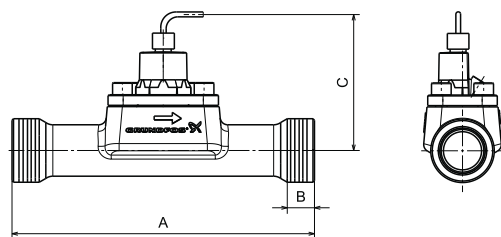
Размеры датчика VFI с резьбовыми соединениями
